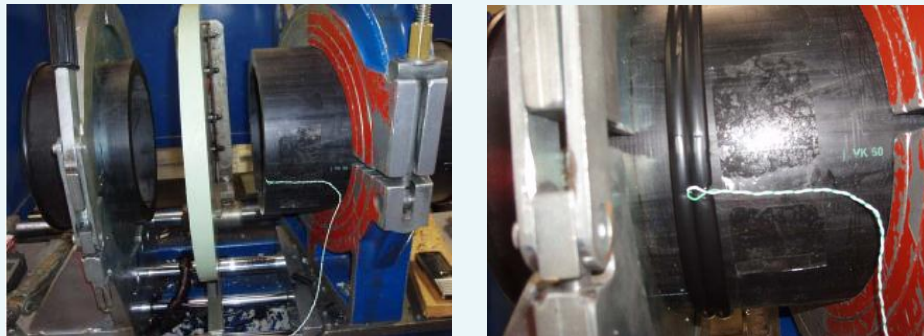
Soldadura de tubos a tope (PLASFLOW)
